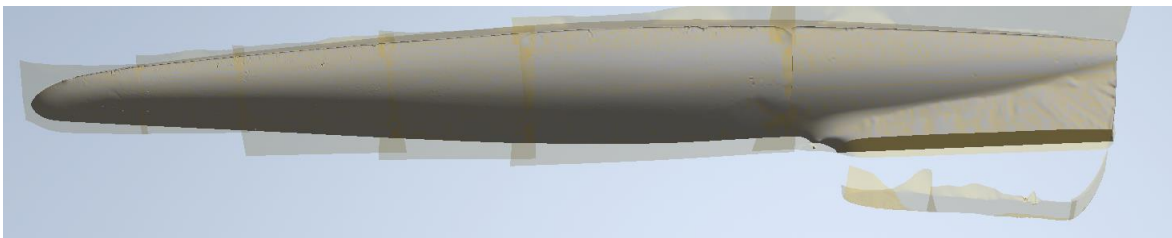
Upravený sken spodní formy – síť (Autodesk Inventor)
